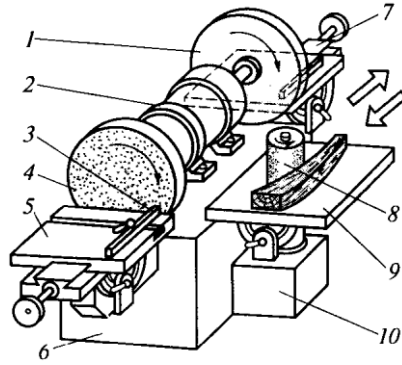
Комбінований шліфувальний верстат з двома дисками і бобіною: 1, 4 – шліфувальні диски; 2 – електродвигун; 3 – напрямна лінійка; 5, 7, 9 – столи; 6 – станина; 8 – бобіна; 10 – кронштейн
